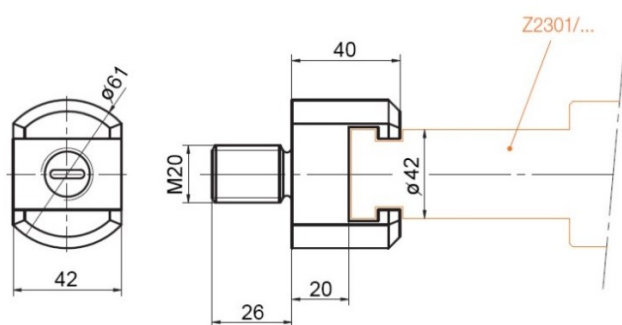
Hydraulický válec Hasco Z2301 [10]
